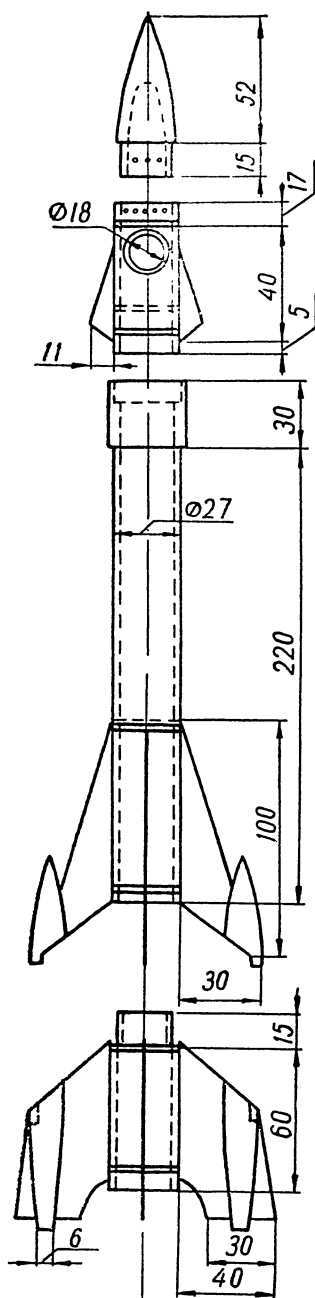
Рабочий чертеж модели двухступенчатой ракеты.
